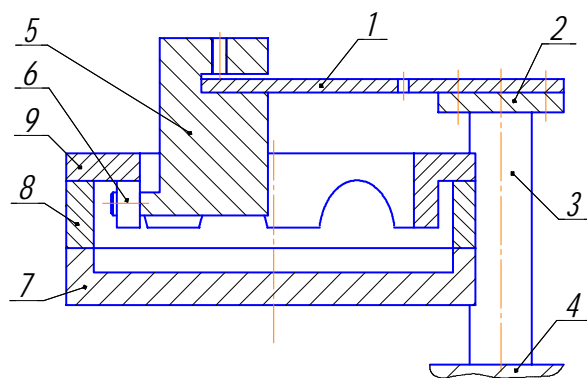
Схема нагружающего устройства для испытаний в РЭМ
